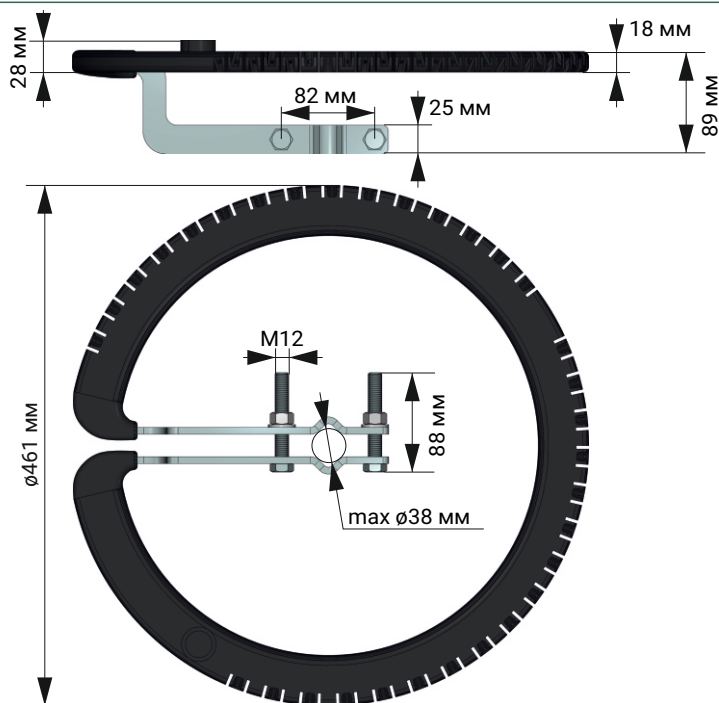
Габаритные и присоединительные размеры разрядного элемента
